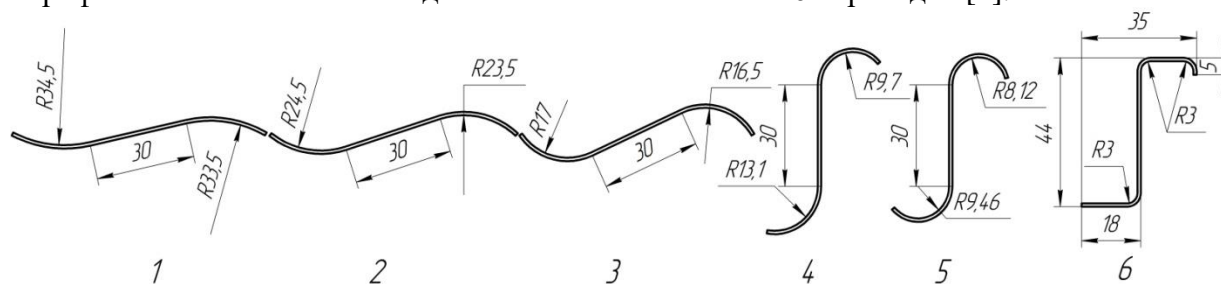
Схема переходов Z-образного профиля для заготовки шпангоута
